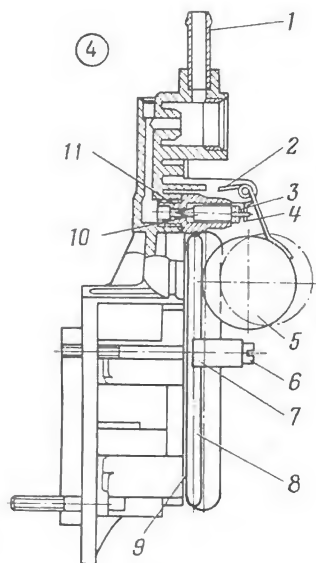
Так проверяют уровень топлива и свободный ход поплавка: 1 — штуцер; 2 — упор; 3 — шарик демпфирующего устройства; 4 — язычок; 5 — поплавок; 6 — винт; 7 — прижимная планка; 8 — стержень; 9 — прокладка; 10 — игла; 11 — седло клапана.
